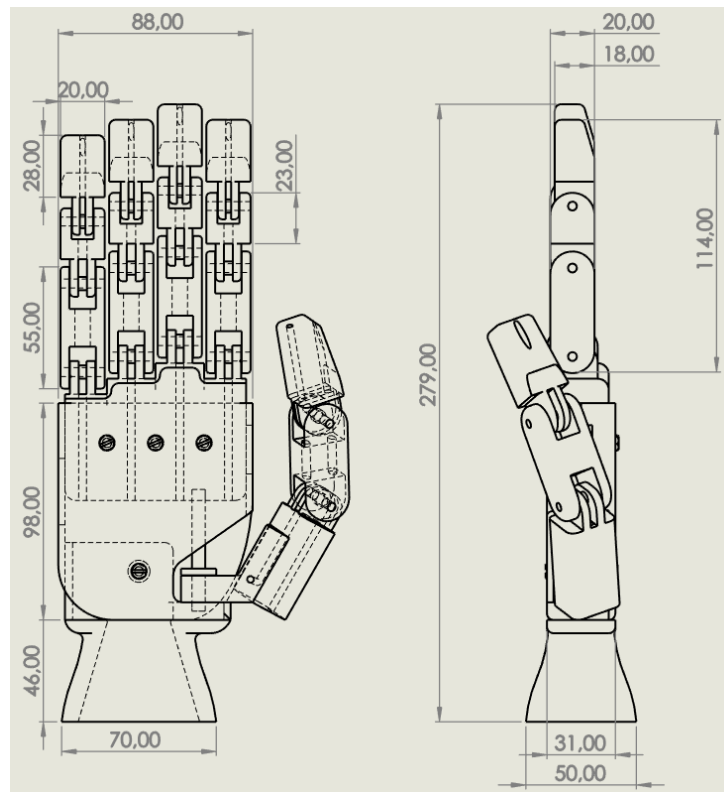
Vista alzado y perfil, y las dimensiones de algunas partes del ensamblaje expresado en mm [Propio]
